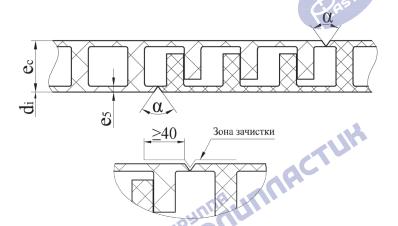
Подготовка скосов кромок перед сваркой наружного и внутреннего стыка и зона зачистки
